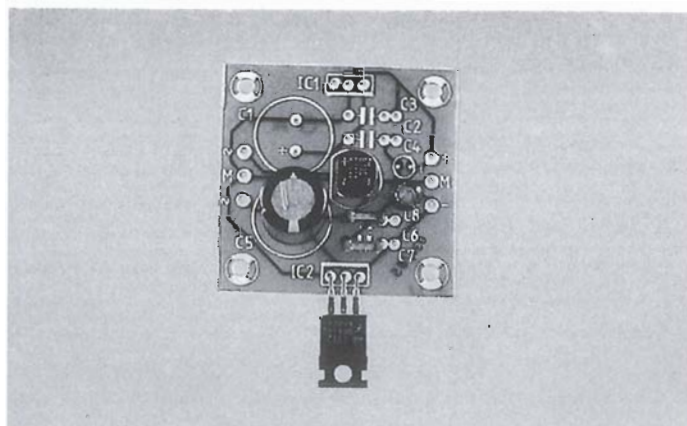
Con este montaje se obtiene una fuente de -12V, 1 A. Si utilizamos esta alternativa deberemos sustituir el condensador C1 por un puente de hilo. La posición IC2 se ha invertido a efectos de identificación. Deberá ser soldado cambiando el orden de sus terminales.
